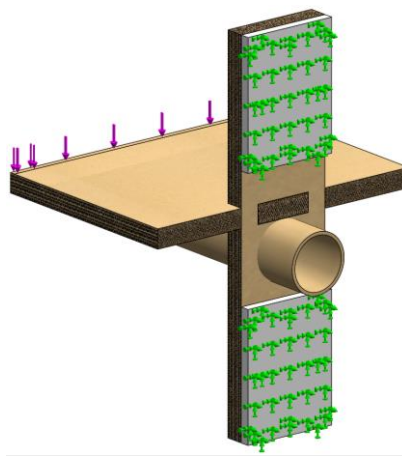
Configuración ensayo de carga estática sobre unión C-PV || Fuente: Elaboración propia
